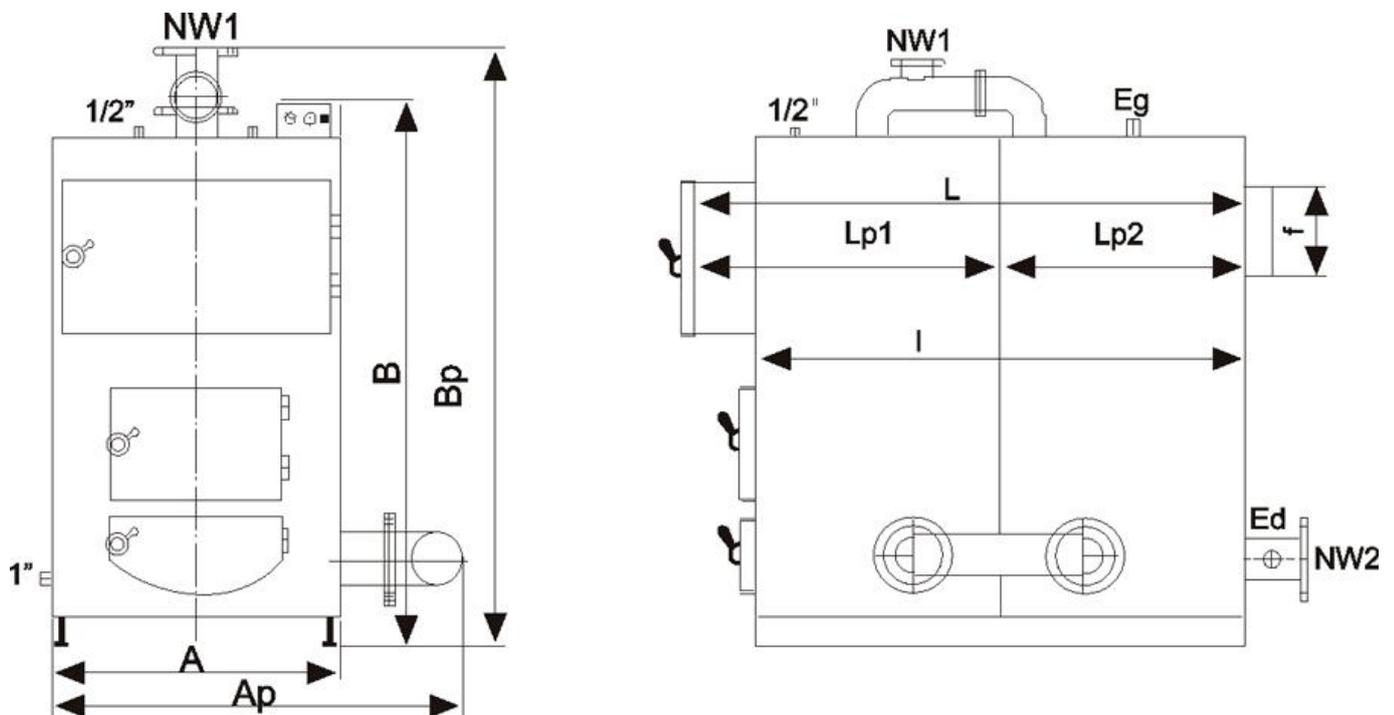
Устройство и габариты компоновки котла Tansan A.E.-900.
